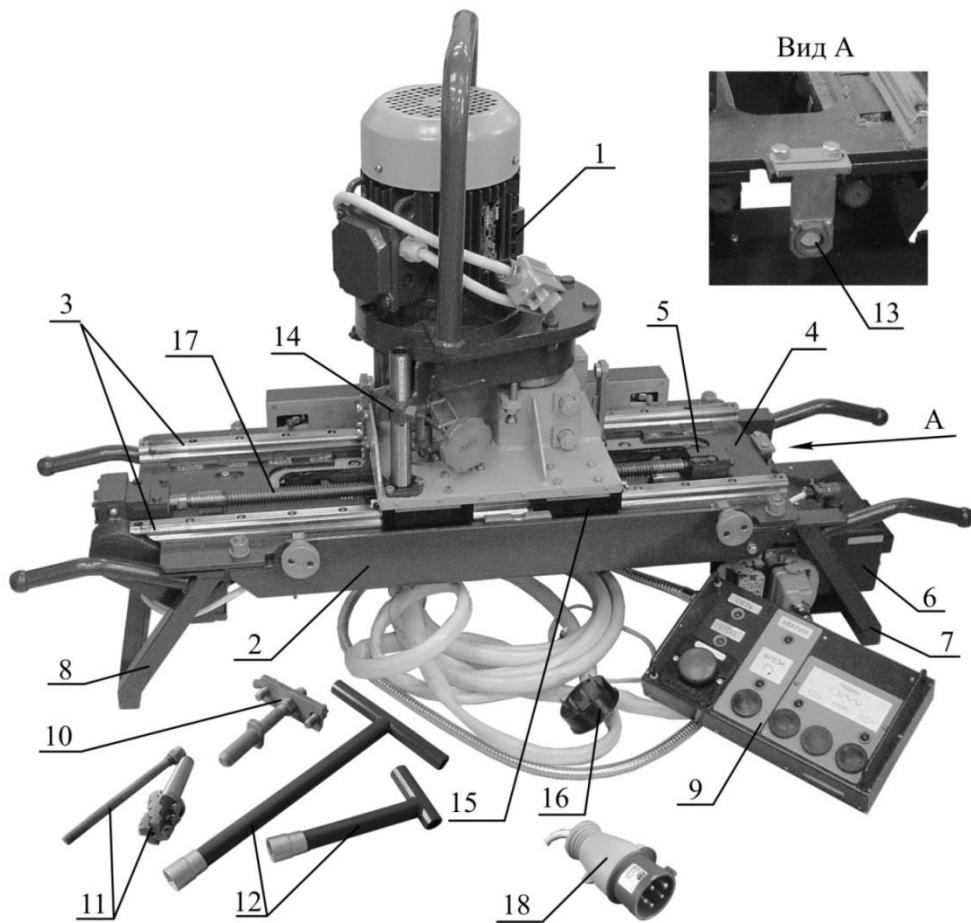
Общий вид станочного модуля МФ-024: 1 - фрезерная головка; 2 - основание; 3 - направляющие; 4 - платформа; 5 - привод каретки; 6 - блок магнитных пускателей; 7 - опора правая; 8 - опора левая; 9 - пульт управления; 10 - технологическая опора установки модуля по месту фрезерования; 11 - фреза с шомполом; 12 - ключ для фиксации зажимов фрезерной головки в стакане каретки модуля (тangenциальных зажимов); 13 - целевой знак платформы; 14 - домкрат; 15 - корпус подшипника направляющей; 16 - силовой кабель с вилкой; 17 - ходовой винт; 18 - вилка силового кабеля
